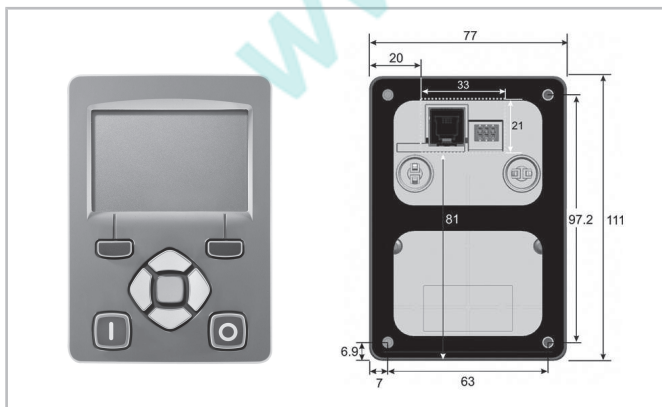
Front- und Rückansicht des Bedienteils mit Befestigungslöchern und Aussparung auf der Rückseite (für externe Montage)
